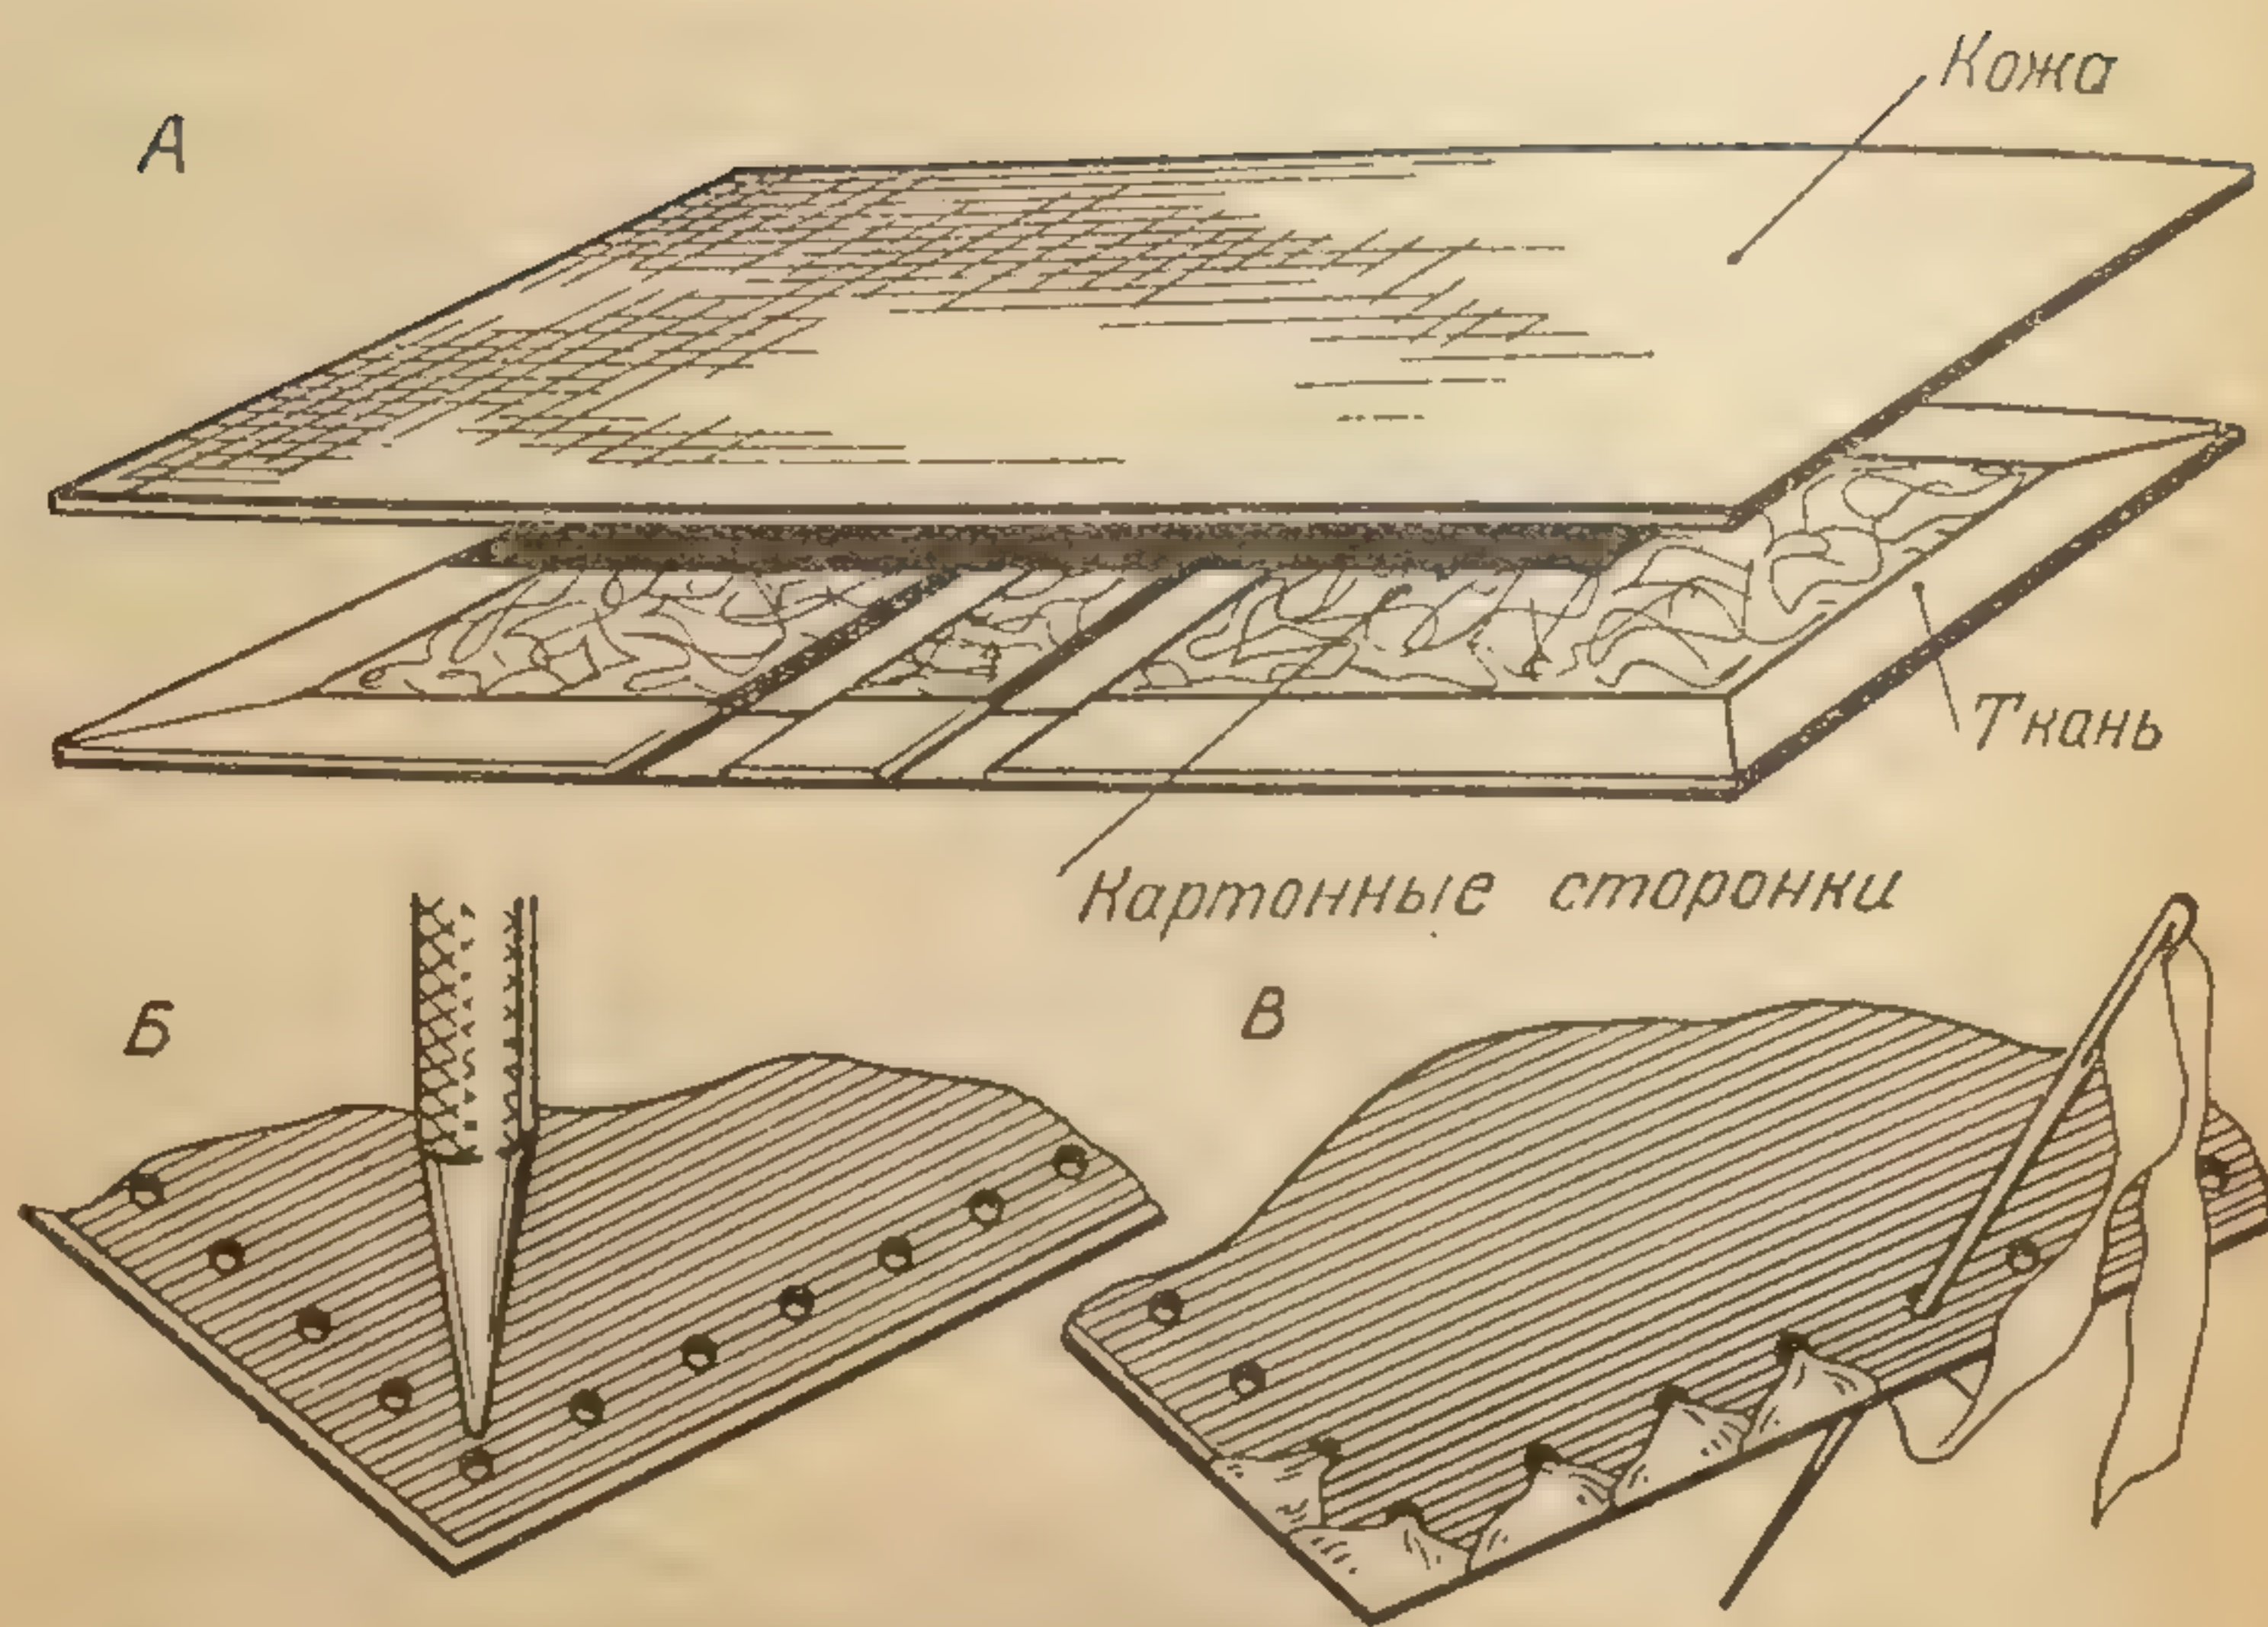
Изготовление крышки для альбома: А — схема расположения деталей; Б — пробивка отверстий на кромке; В — обшивка крышки
